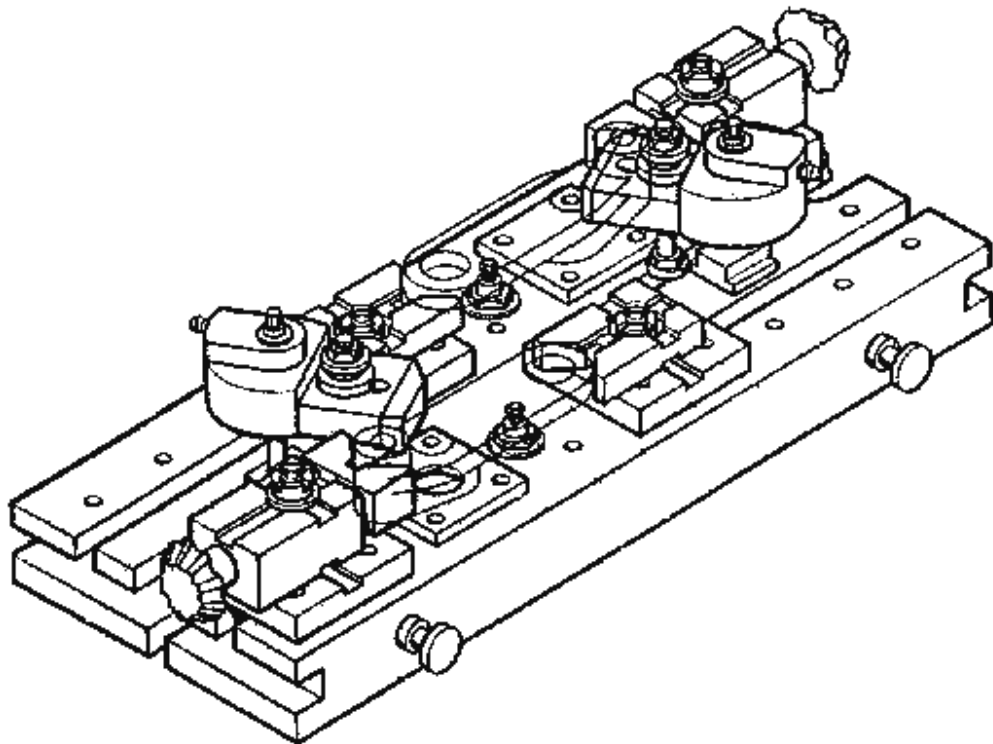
Компоновка двухместного приспособления СРП для обработки рычагов
